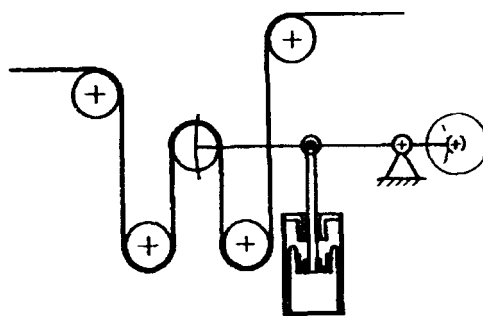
Качающийся валик-датчик, нагруженный пневмоцилиндром.
